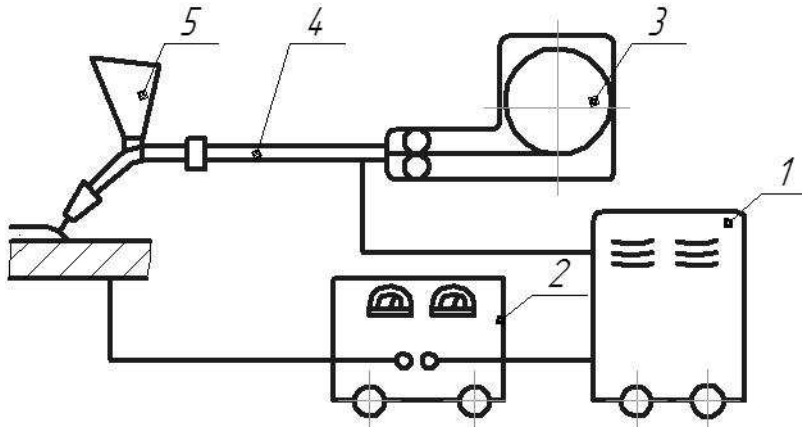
Устройство полуавтомата для сварки под слоем флюса:
